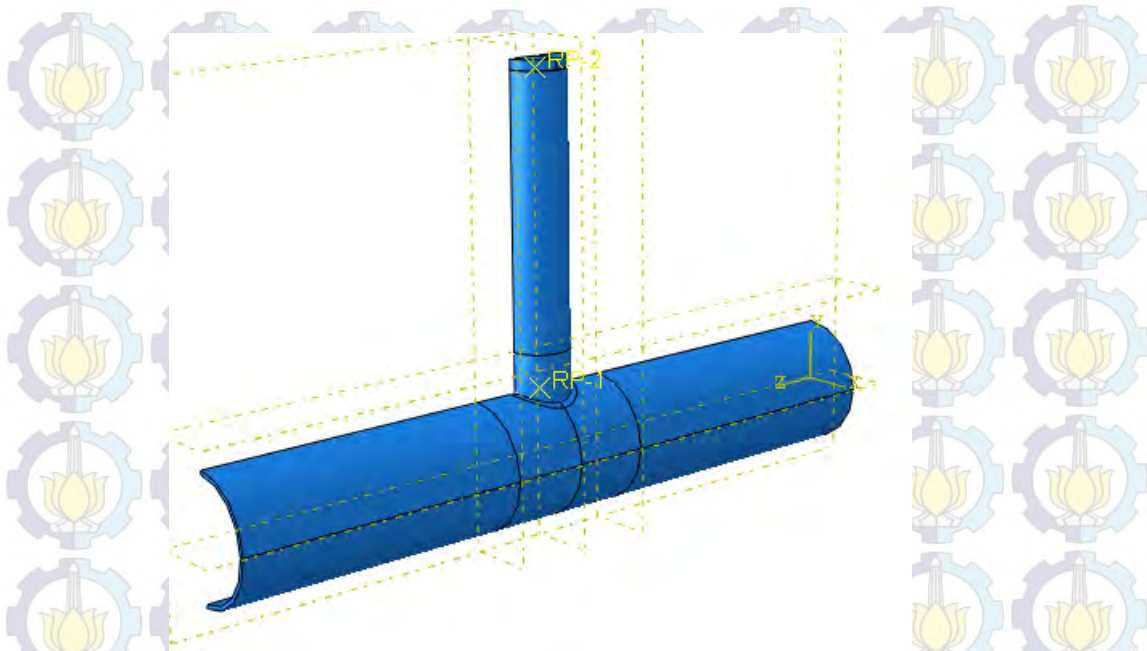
Cross Section Penampang Pipa baja dalam program
